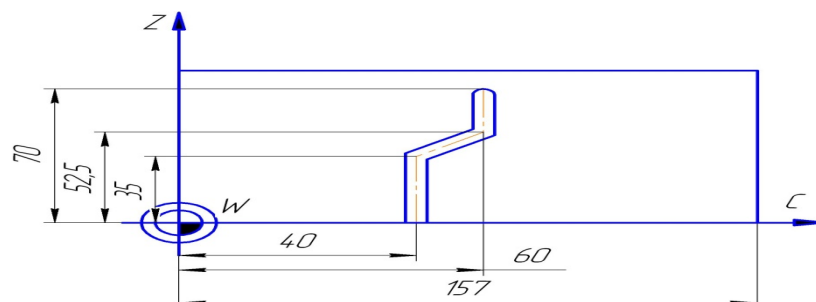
Незамкнутый контур детали, расположенный на цилиндрической поверхности
